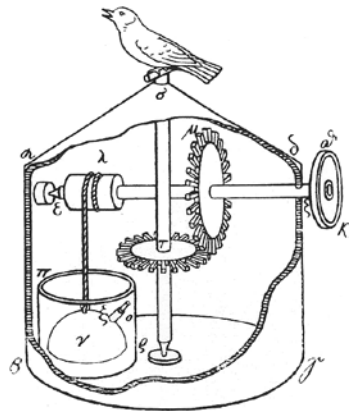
Automatenpielzeug mit einem Winkelgetriebe
